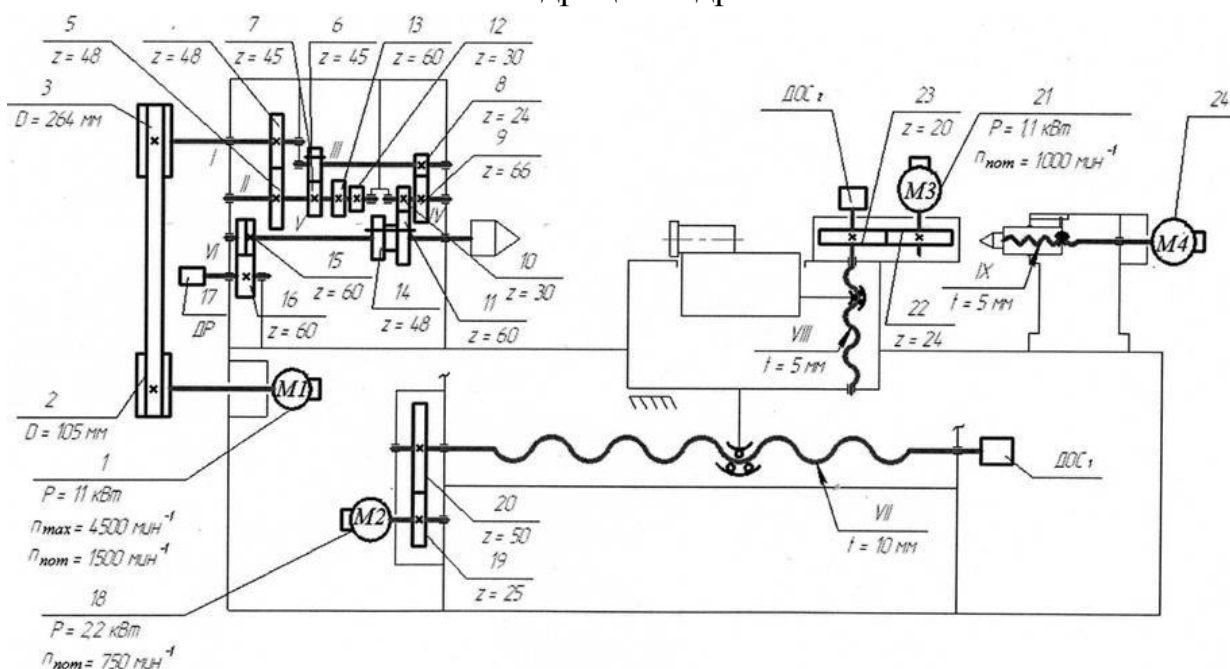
Кинематическая схема привода главного движения токарного станка с ЧПУ – переключение скорости блоками колес
